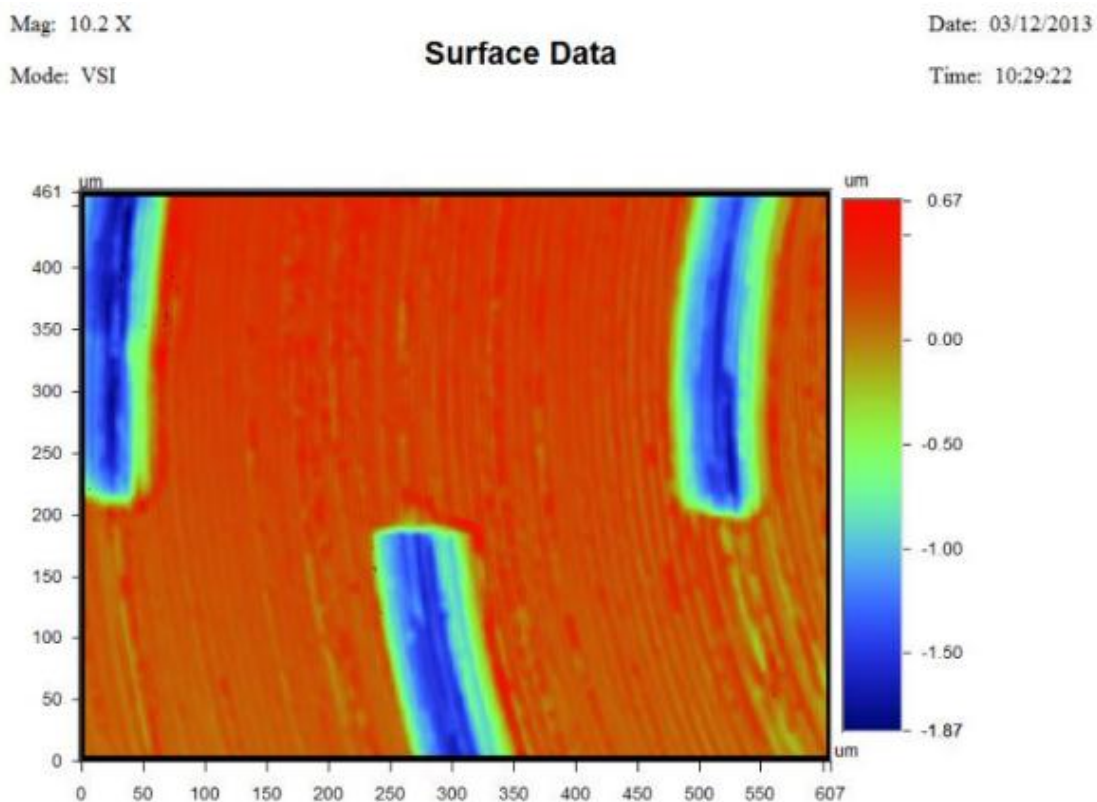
Vista superior da superfície usinada com onda quadrada e avanço de 0,25 mm/volta.
